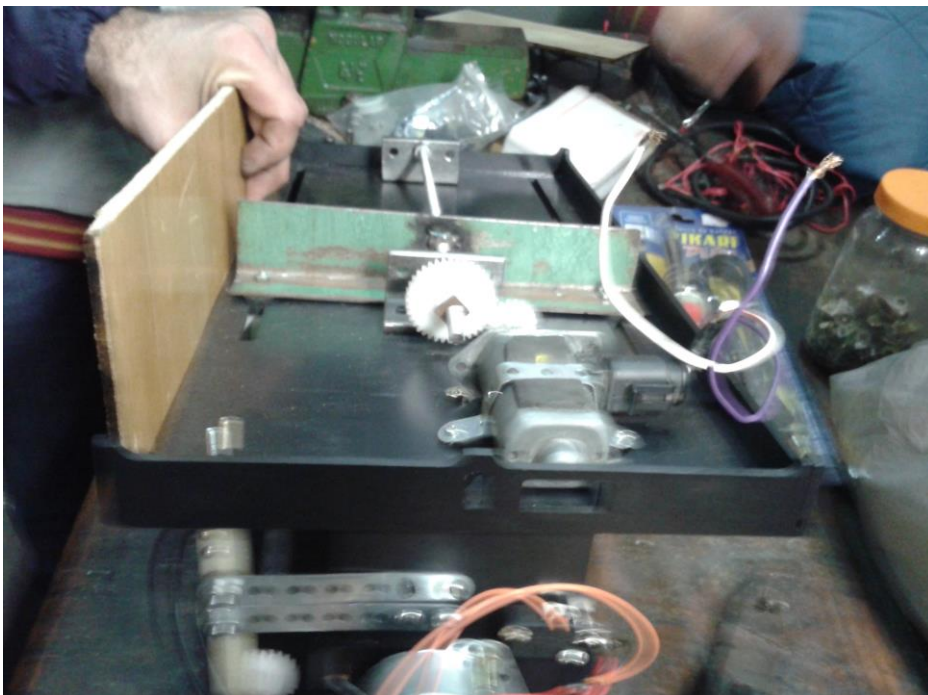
Segundo Motor DC 12V visto por outro ângulo
